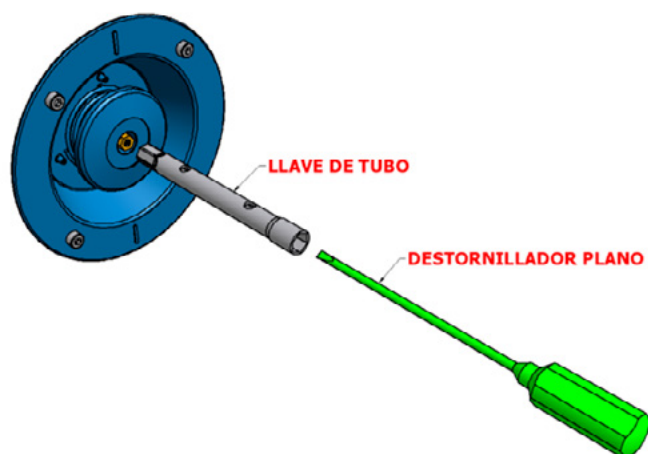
Explosionado Bandeja + Llave + Destornillador
